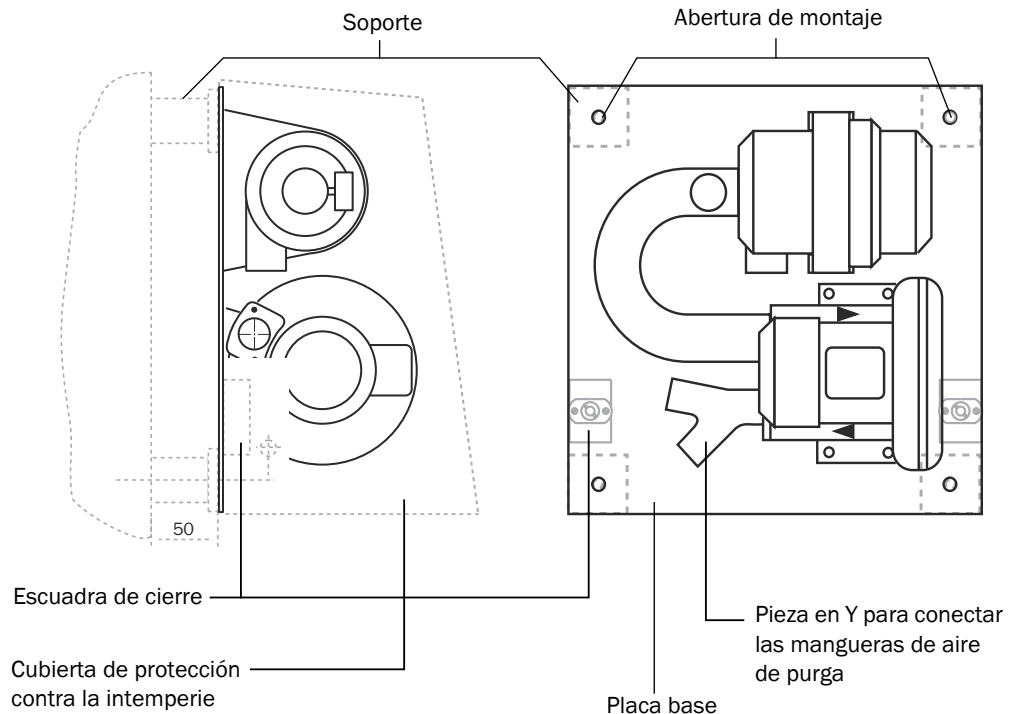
Montaje de la unidad de aire de purga SLV 4
